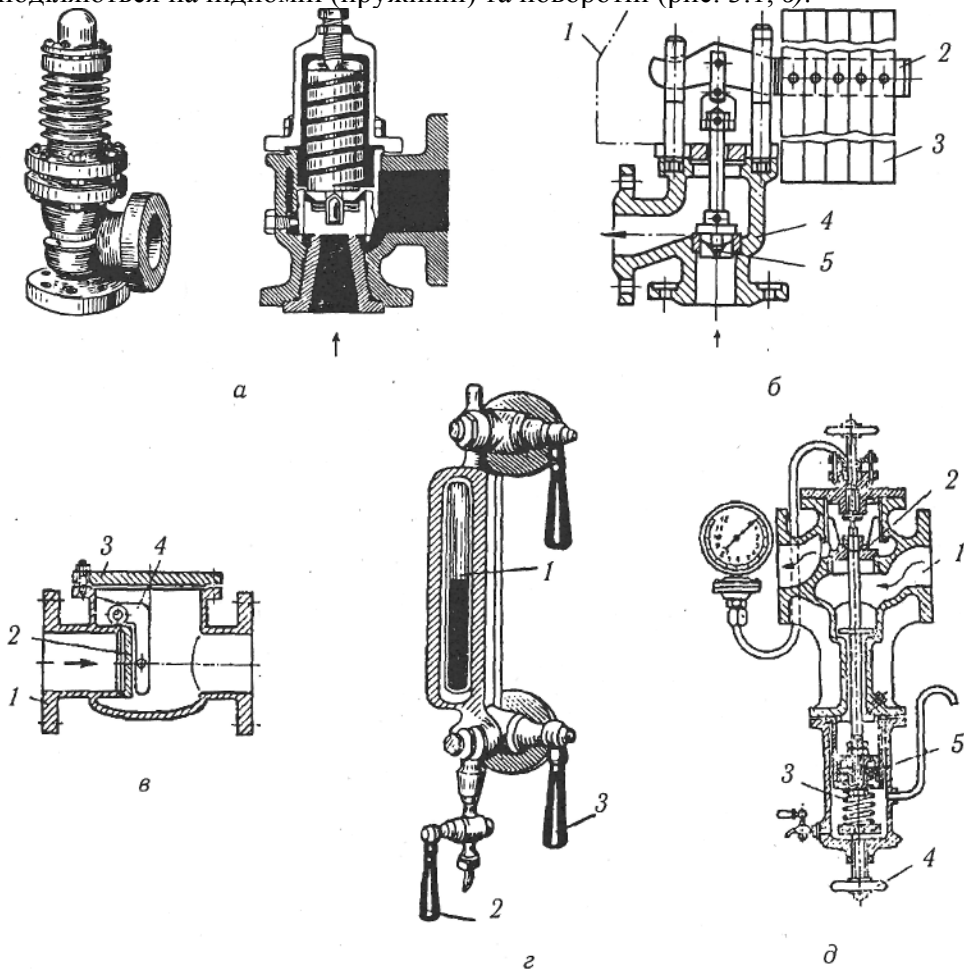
Контрольно-вимірювальні прилади та запобіжні пристрої: *a* — пружинні запобіжні клапани; *б* — важільно-вантажний запобіжний клапан: 1 — кожух; 2 — важіль; 3 — вантаж; 4 — сідли; 5 — золотник; *в* — поворотний зворотний клапан: 1 — корпус; 2 — засув; 3 — кришка; 4 — серга; *г* — показчик рівня води: 1 — скло; 2 — ручка спускного крана; 3 — ручка запірного крана;
